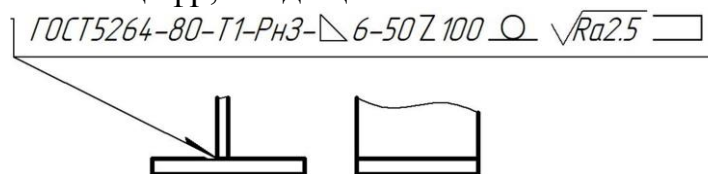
Пример условного обозначения сварного шва
